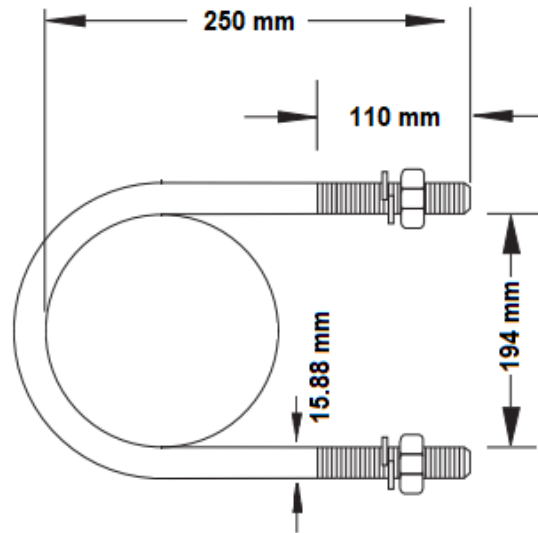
Detalle y dimensiones Abrazadera U
